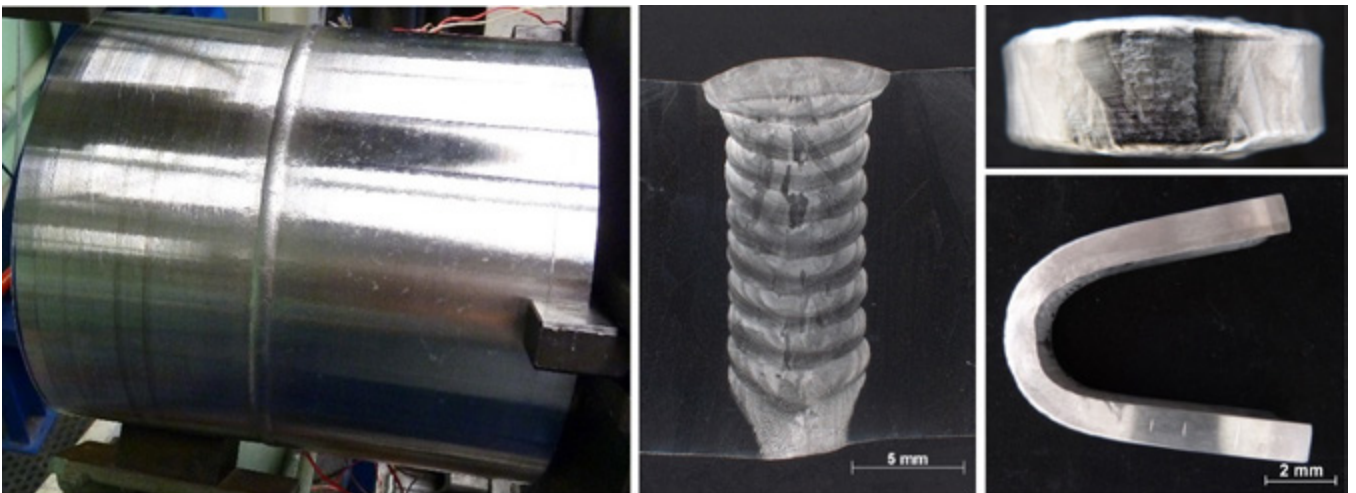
Vollmechanische WIG-Schweißung als Rundnaht am Schleudergussrohr aus der Nickelbasislegierung Alloy 617 (links), Makroschliff der Schweißnaht (Mitte) und bestandene Seitenbiegeprobe (rechts).
